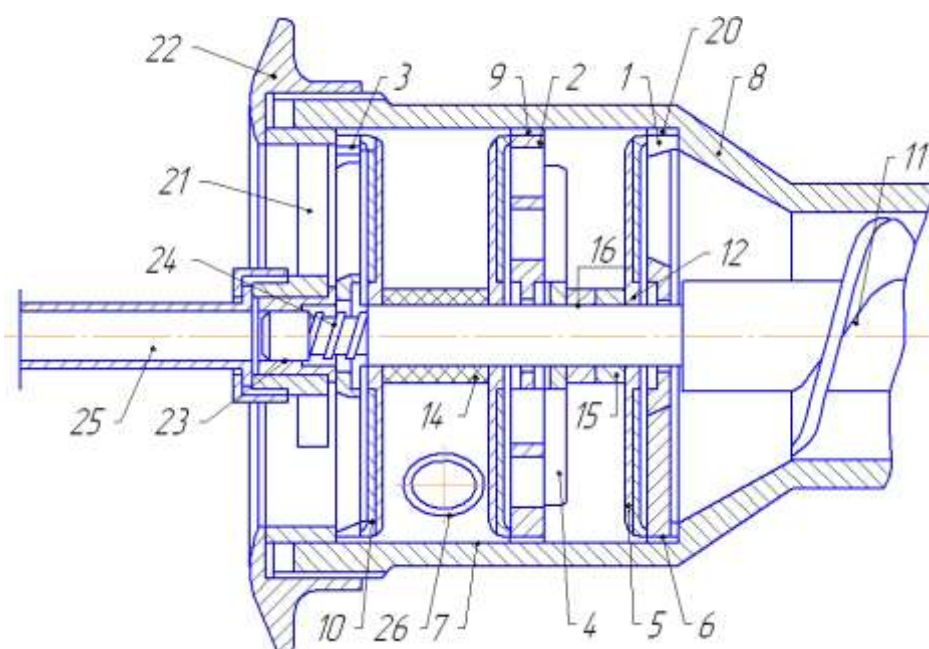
Ріжучий вузол подрібнювача: 1, 2, 3 – ґрати; 4 – правосторонній ніж; 5 – лівосторонній ніж; 6 – радіальний зуб; 7 – паз; 8 – корпус; 9 – поздовжня вставка; 10 - ножовий вал; 11 – шнек; 12 - маточина; 13, 16 – фаска; 14, 19 – втулка; 15 - розпірна втулка; 17 – приплив; 18 – вставка; 20 – амортизатор; 21 - прижимна вставка; 22 – гайка; 23 - підшипник; 24 – виток; 25 - трубопровід; 26 - патрубок; 27 – пластина
